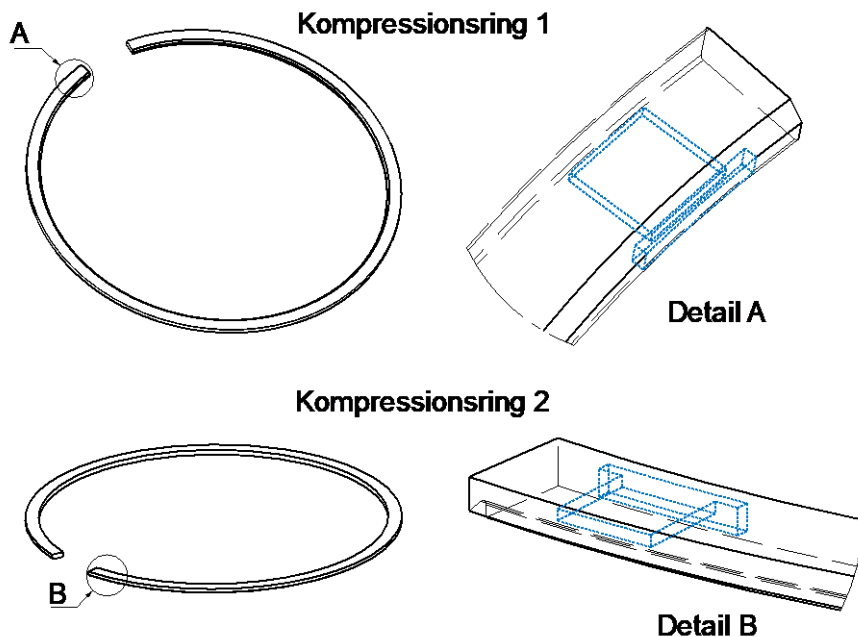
Bearbeitung der Kolbenringe zur Aufnahme der Radioisotope nach [56].
